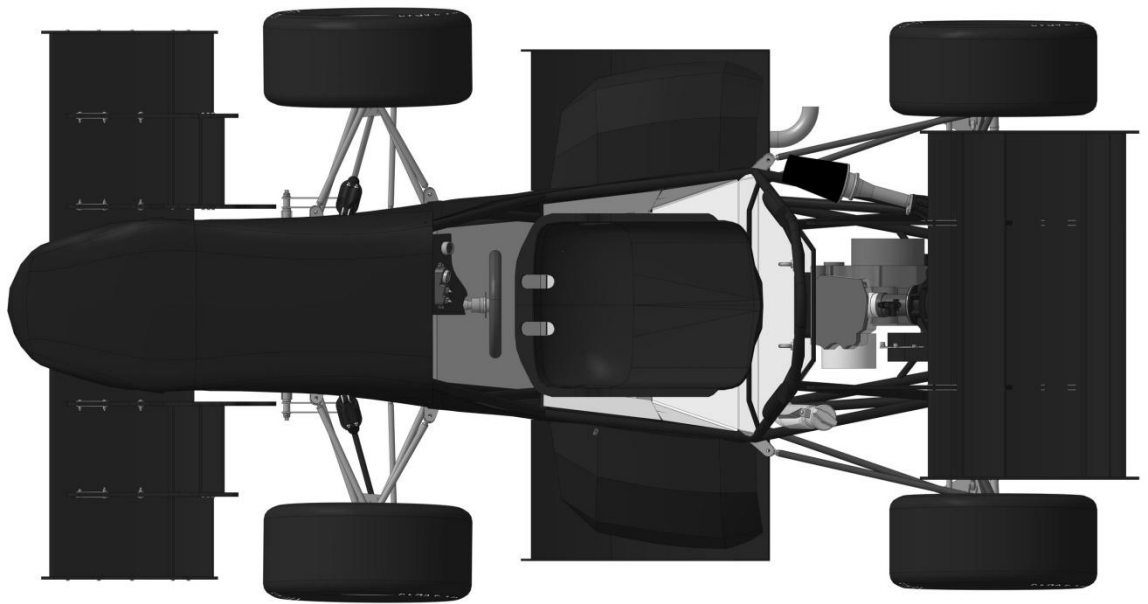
3D-модель гоночного болида, вид сверху
